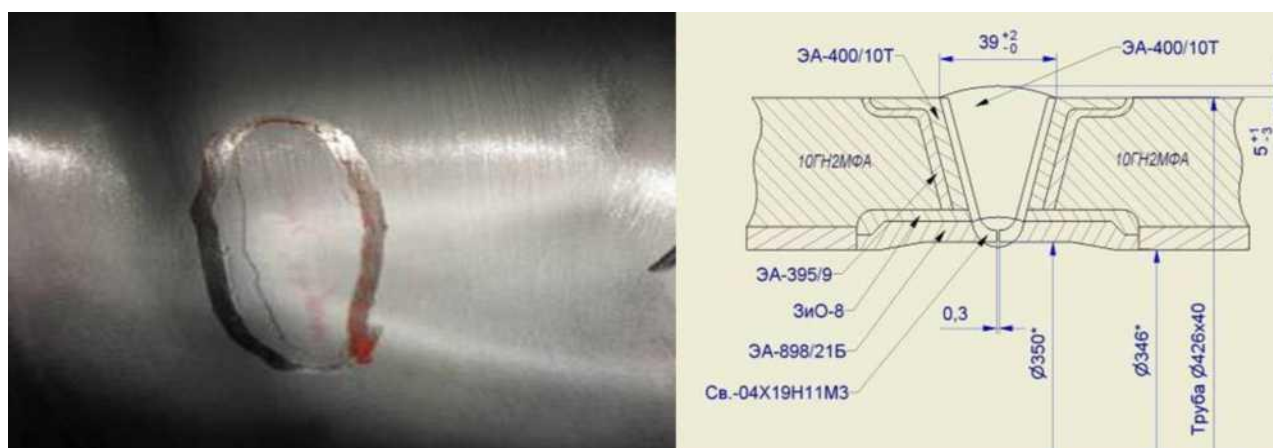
Дефект композитного сварного соединения №7 дыхательного трубопровода компенсатора давления 5-го блока НВАЭС
